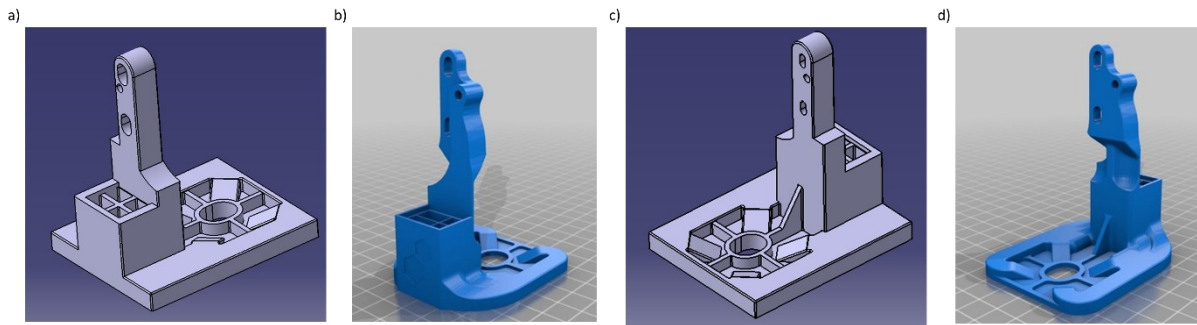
Vue comparative entre la nouvelle version du support de ventilateur et la version fournie par DyzeDesign (a) Vue arrière du nouveau support (b) Vue arrière du support DyzeDesign (c) Vue avant du nouveau support (d) Vue avant du support DyzeDesign
